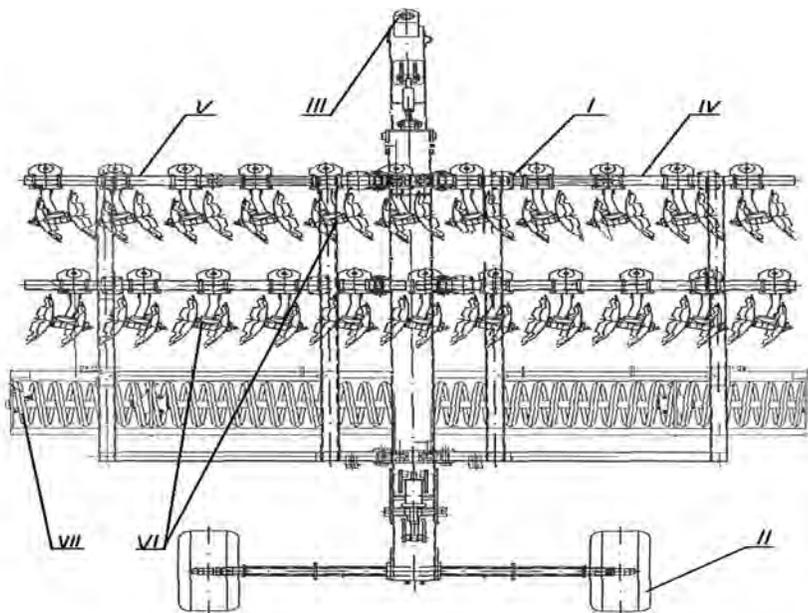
Борона БДК-5,4 в рабочем положении:
